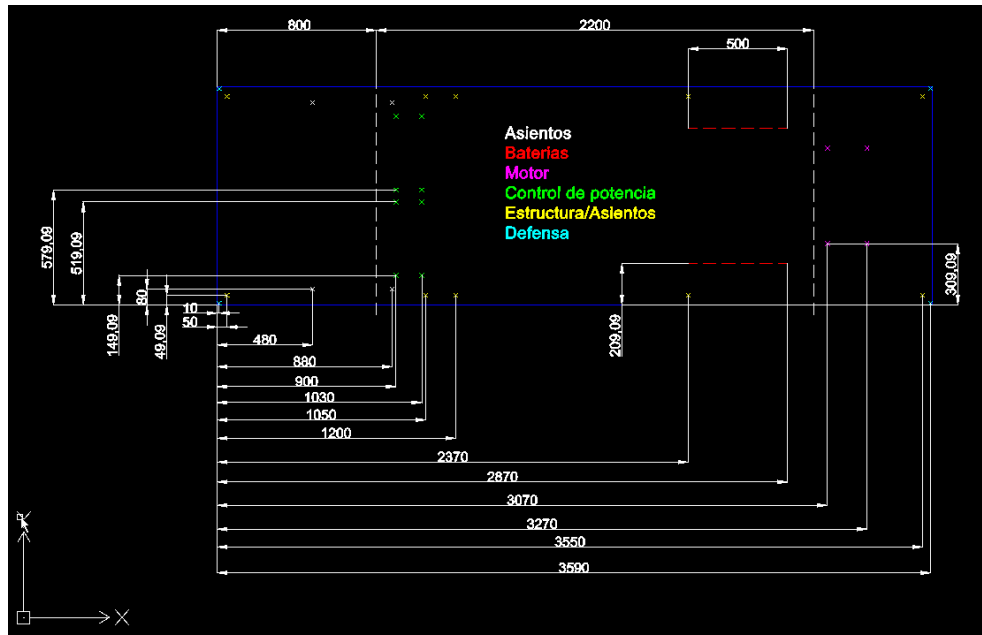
Posición final de la fuerza ejercida por cada componente sobre la placa.
